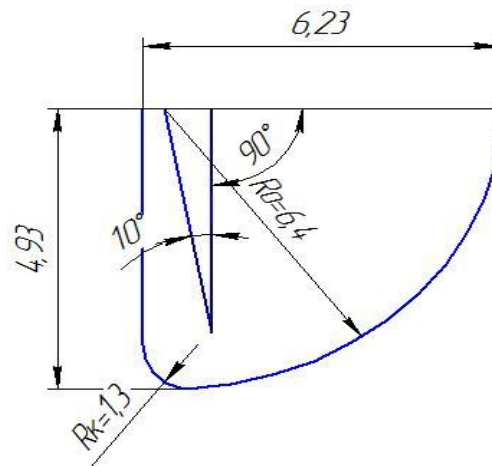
Размеры фрезы под сверло
